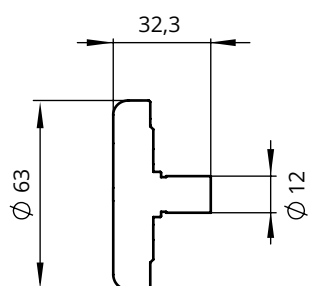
Dimensions en mm · Types 3374-25 et -27, exécution Forme A
